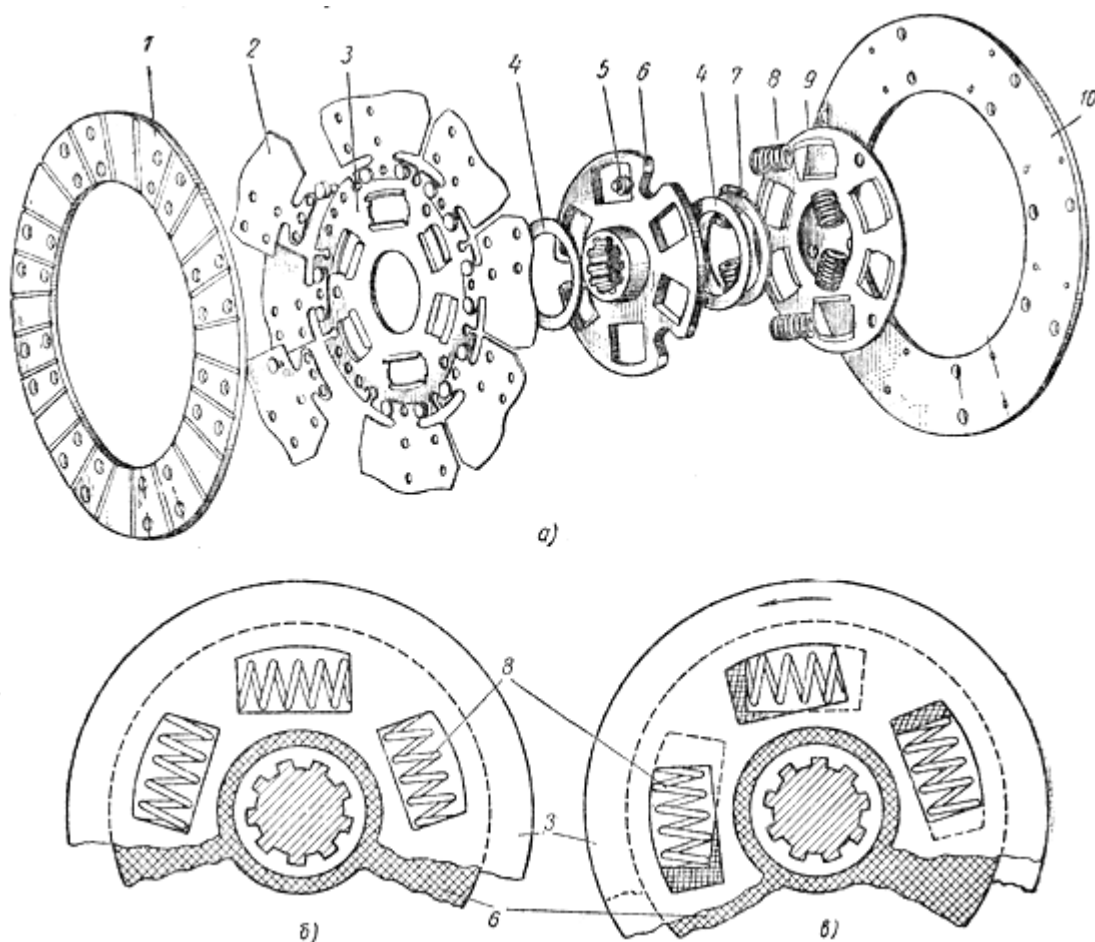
Детали ведомого диска сцепления и схемы работы гасителя крутильных колебаний
